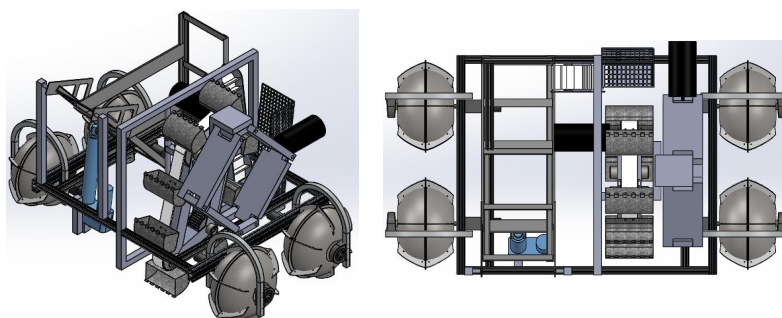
Diseño final subsistema mecánico. Vista isométrica (izquierda) y vista superior (derecha)
